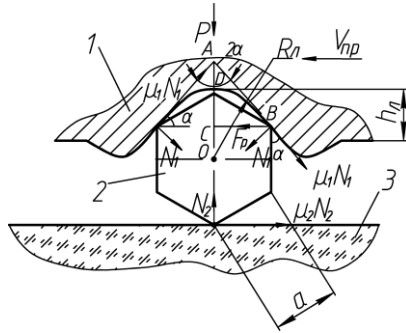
Схематическое представление диаметрального сечения наплывов металла и форма образуемой ими поверхности по краю лунки
